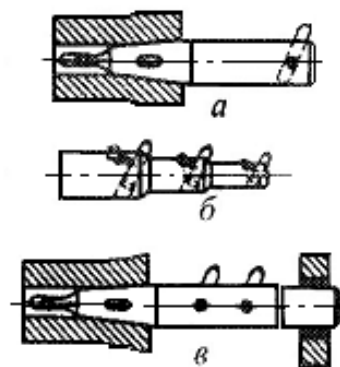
Види борштанг, які застосовуються на розточувальних верстатах
